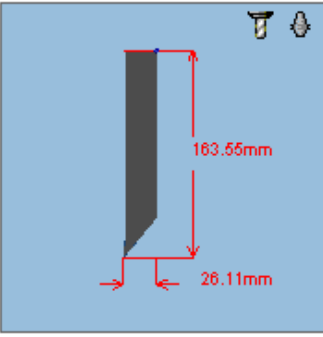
Державка різця «CP-25BR-2525-12»
